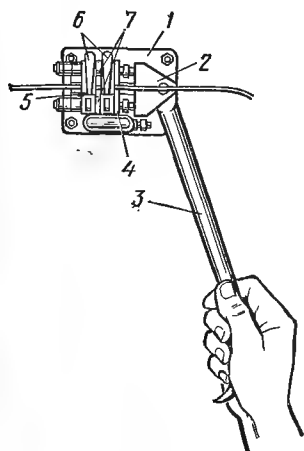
Настольный сварочный станок СНС-3:
